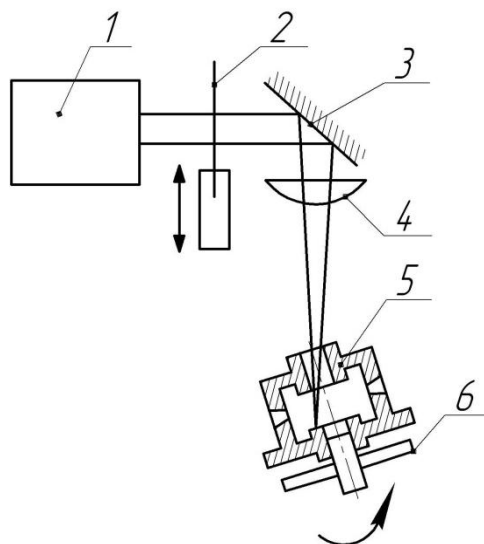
Схема обробки деталі газовим лазером на CO₂:
